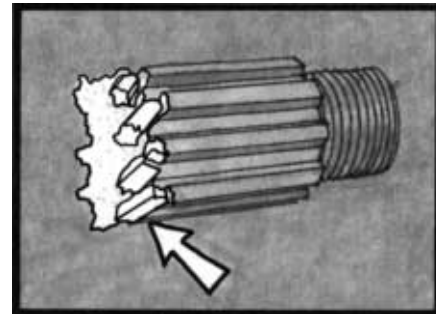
Неровный срез вала является признаком чрезмерного крутящего момента.
